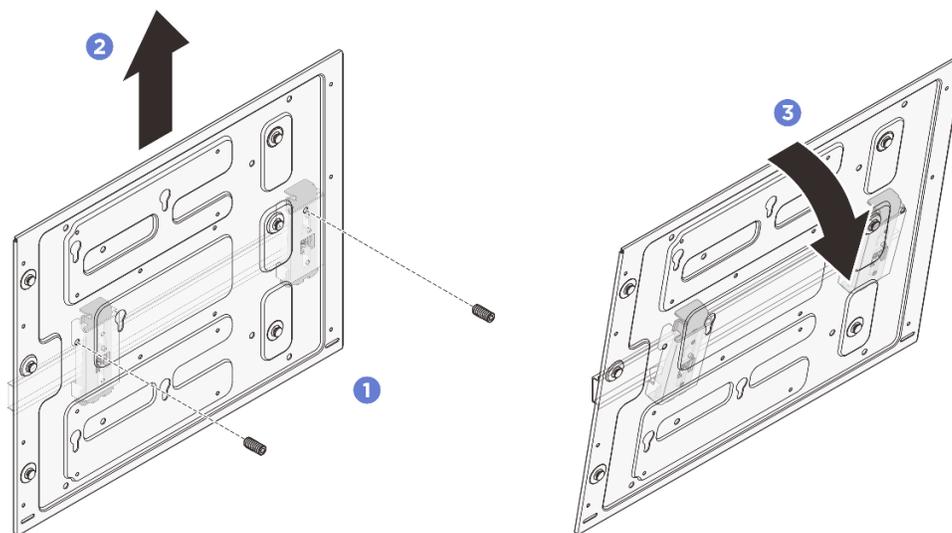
Снятие пластины для монтажа на DIN-рейке
